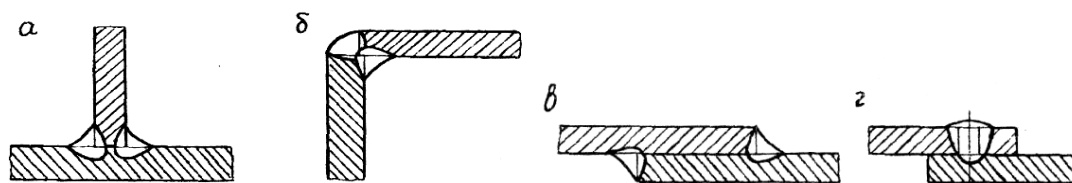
Виды сварных соединений: тавровое (а); угловое (б); нахлесточное с угловыми (в) и пробочными (г) швами
